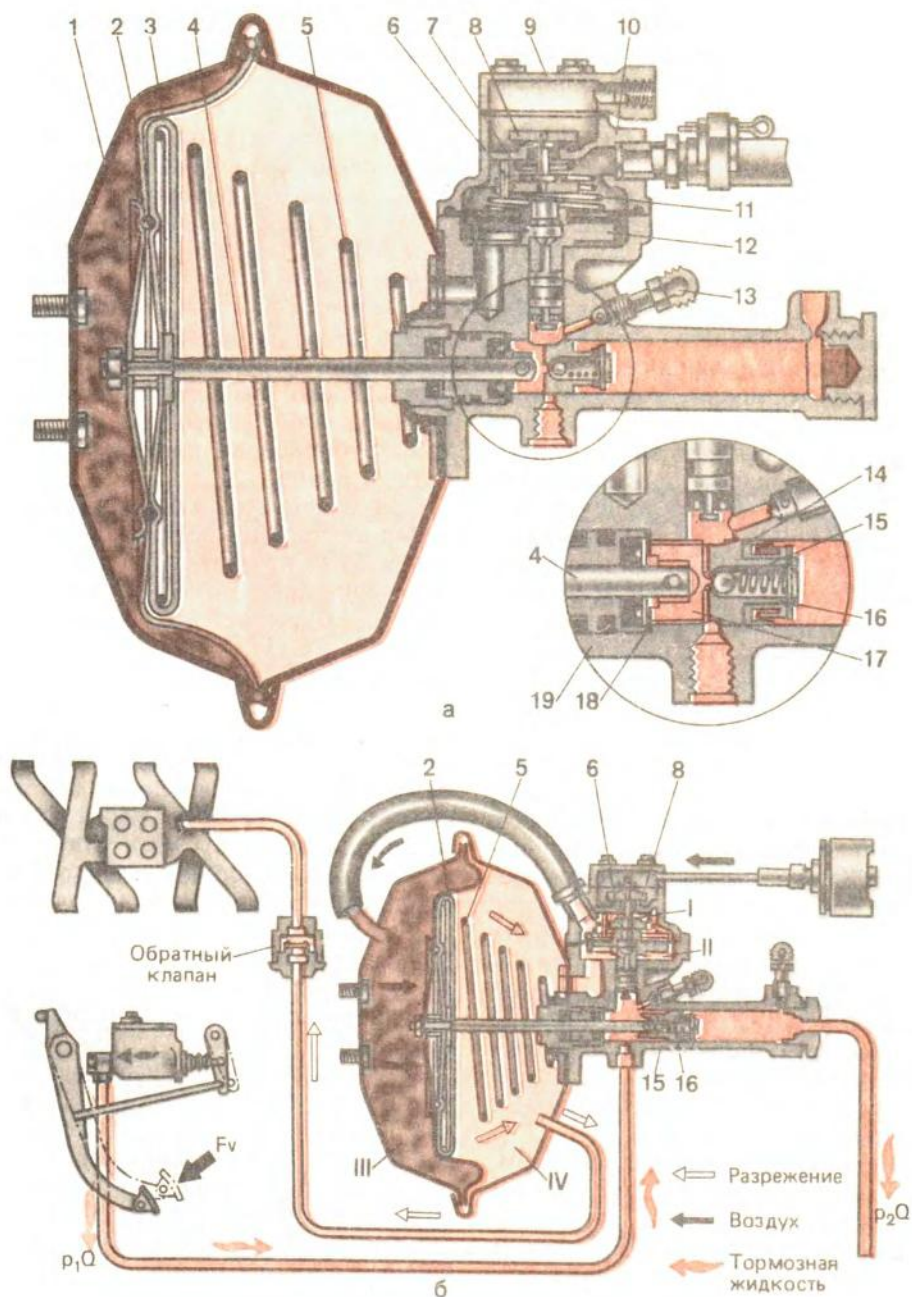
Гидروвакуумный усилитель тормозного привода автомобиля ГАЗ-66:
